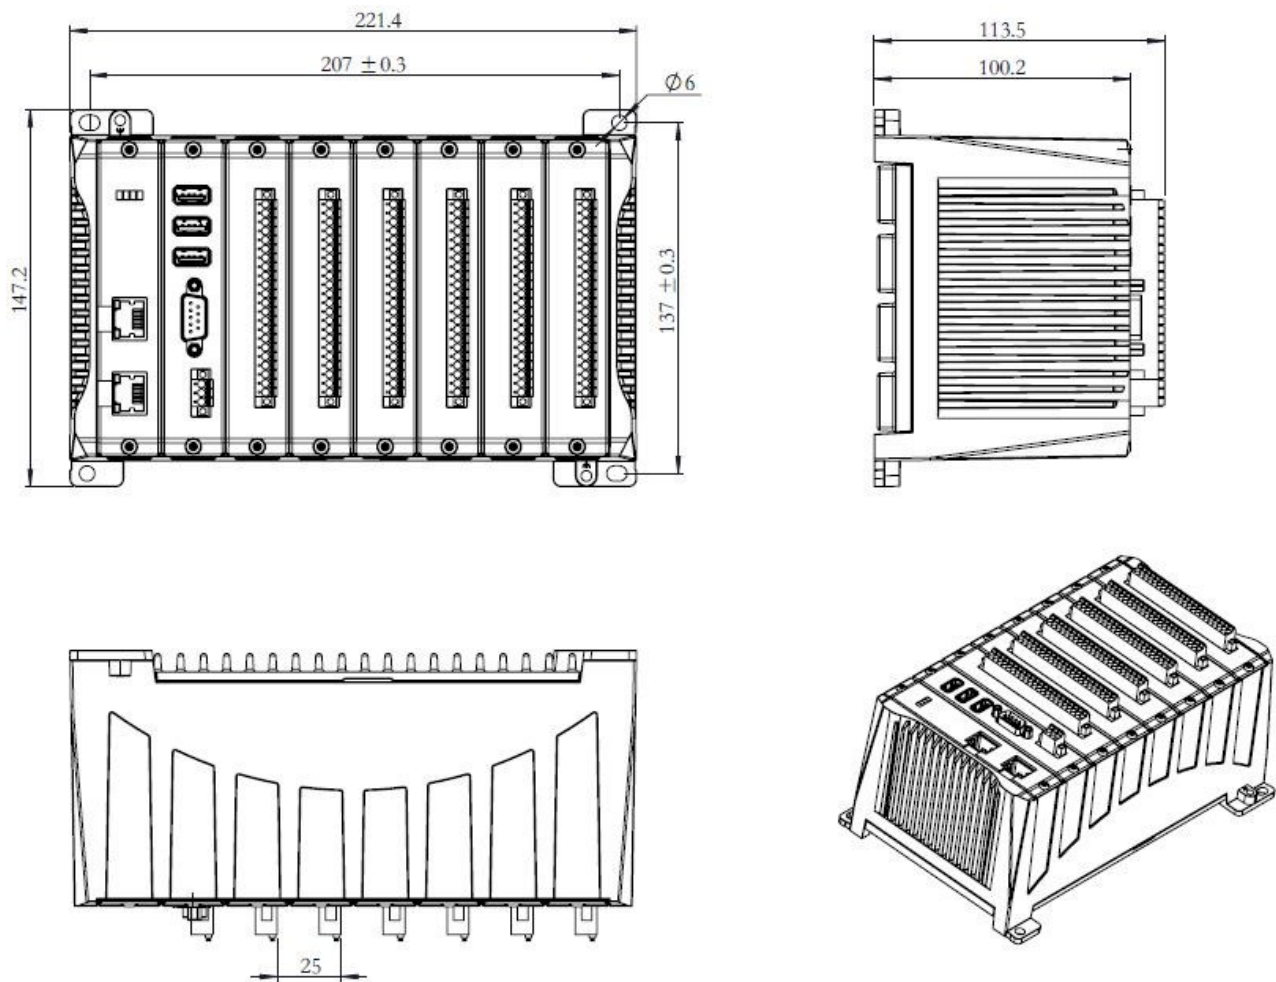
GEM 系列控制器尺寸图 单位 (mm)
